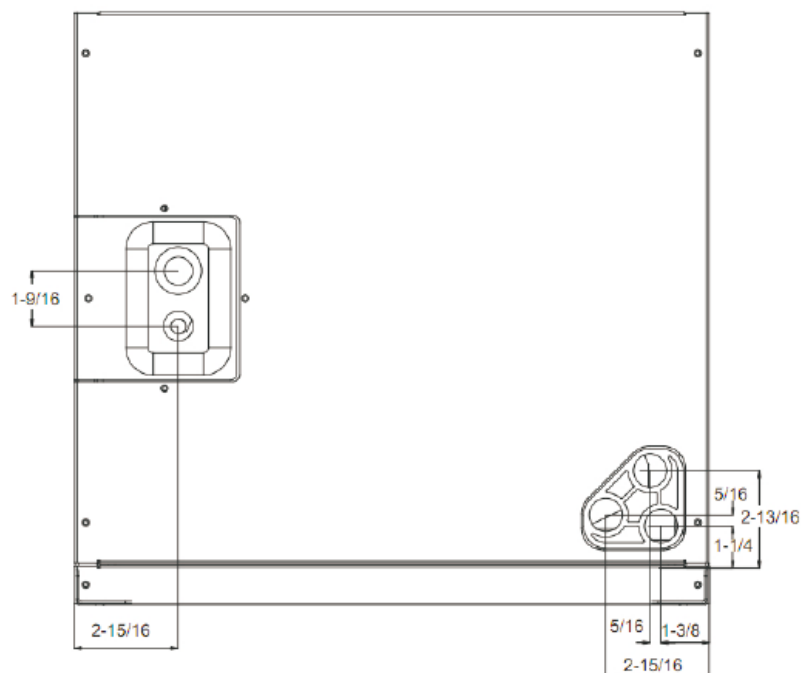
DIMENSIONES PARA EL SERPENTÍN DE CONEXIÓN FRONTAL
